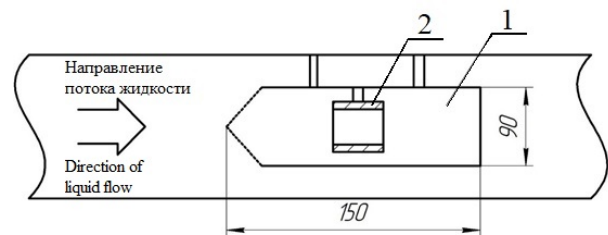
Расположение трубы Шаубергера внутри измерительной трубы: 1 – труба Шаубергера; 2 – втулка с оптической системой
